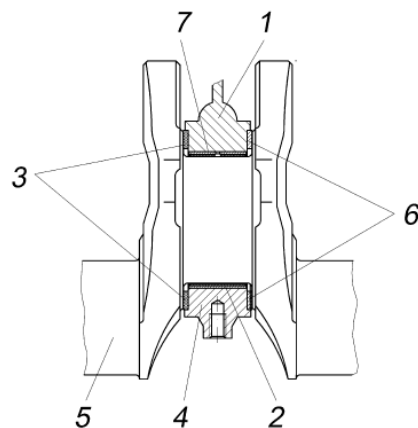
Середній або упорний підшипник колінчастого вала:
